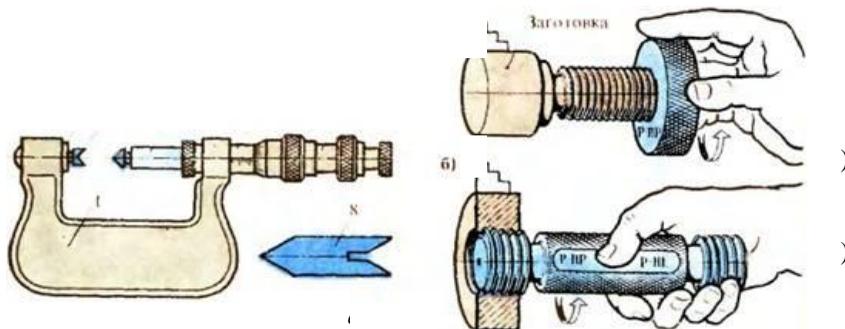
Контроль параметров резьбы: а – резьбовым микрометром;
